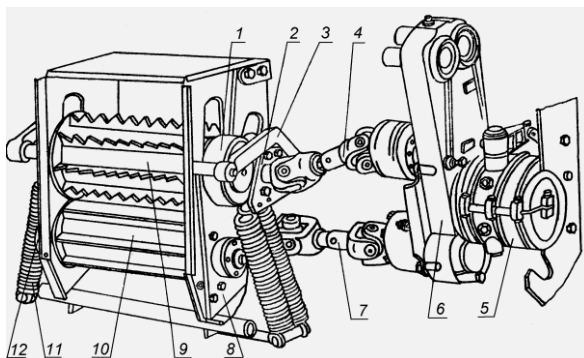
Питающий аппарат: 1 – редуктор верхних валцов; 2 – навеска; 3 – рычаг; 4, 7 – карданный вал; 5 – коробка передач; 6 – редуктор; 8 – корпус; 9 – верхний валец; 10 – нижний валец; 11 – пружина; 12 – редуктор нижних валцов
